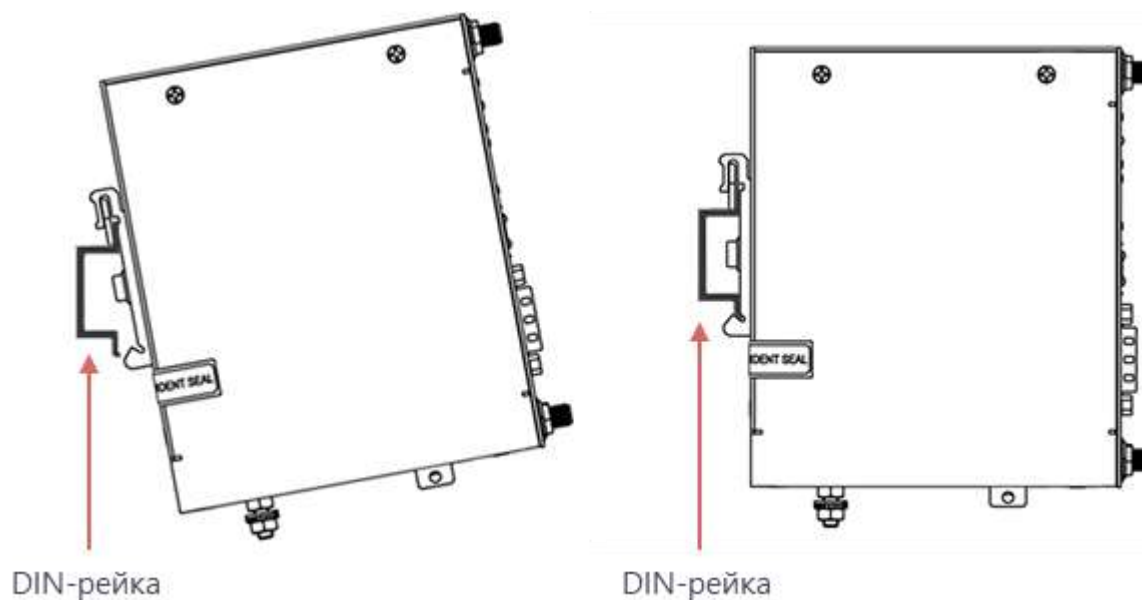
Установка ViPNet Coordinator IG на DIN-рейку
